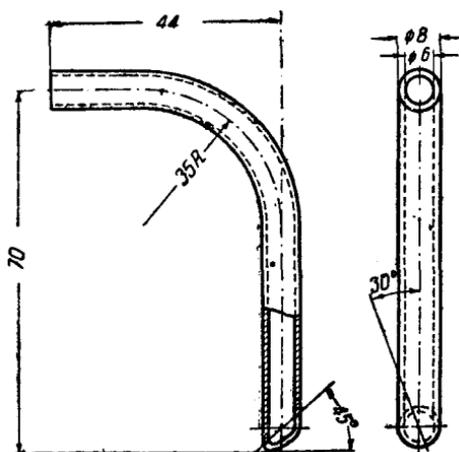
Дет. № 335. Воздушная трубка в крышку поплавковой камеры
